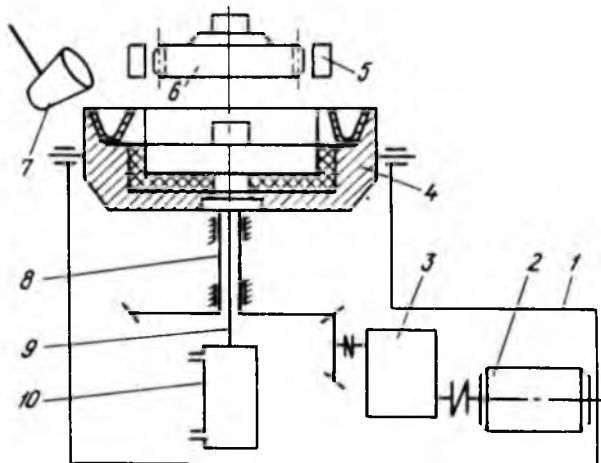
Схема установки для восстановления звездочек цепных передач заливкой жидким металлом:
